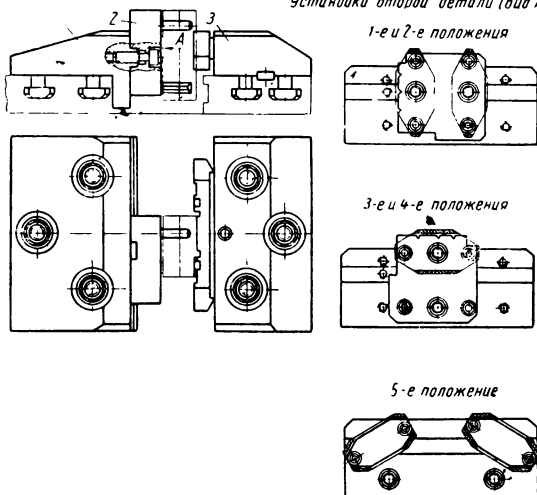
Схемы установки двух различных деталей в пяти положениях в сменной наладке к тискам УПГ-2:
